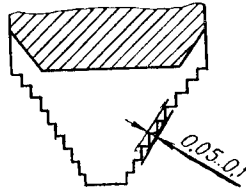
Прорізний зуб дискової чорнової модульної фрези
